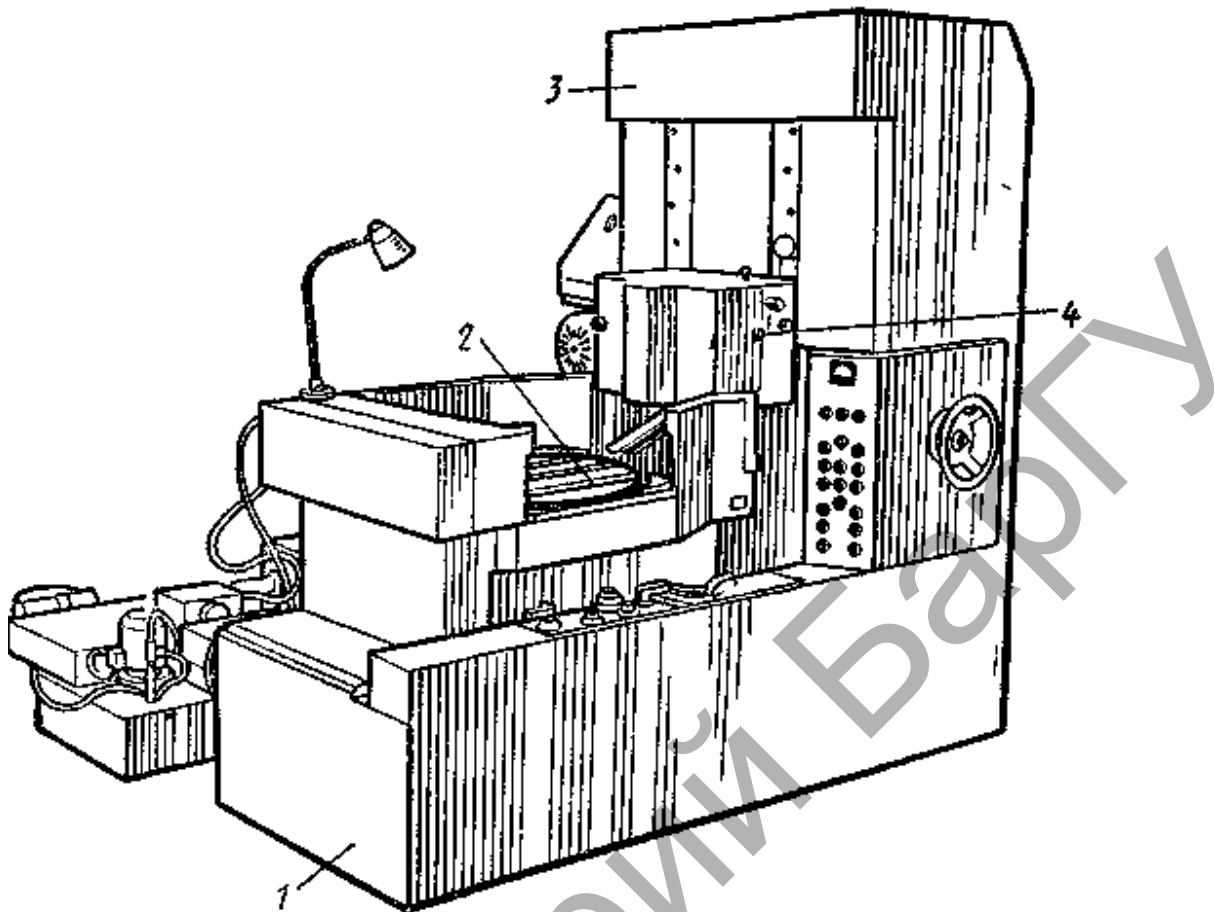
Общий вид плоскошлифовального станка с круглым столом
